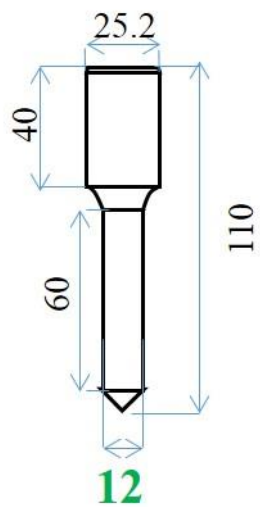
金属製鈎 4 の概要図 (単位 : mm)
